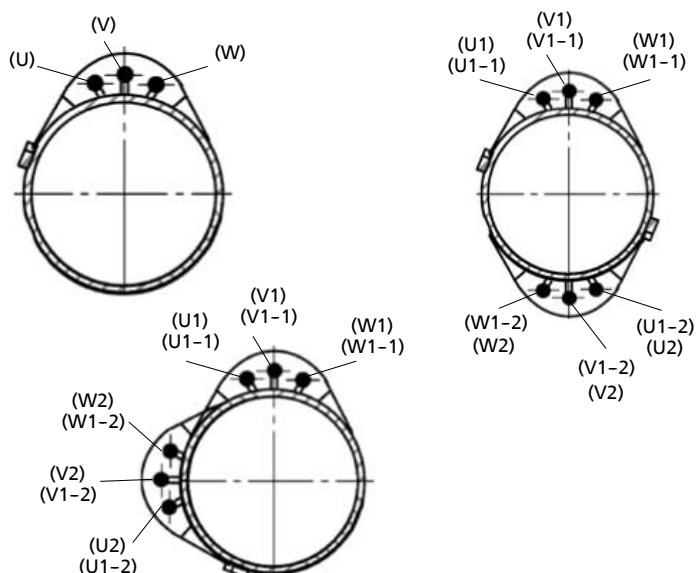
Размещение трех и шести отдельных проводов на нагнетательном трубопроводе
